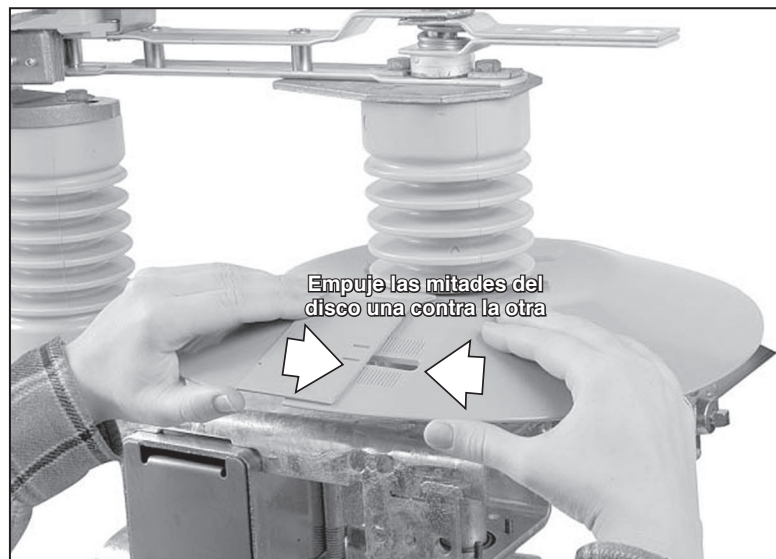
Empuje las mitades una contra la otra. Cierre a presión la lengüeta superior para que quede en su lugar. Las mitades del disco deben quedar tan apretadas como sea posible alrededor del aislador.
